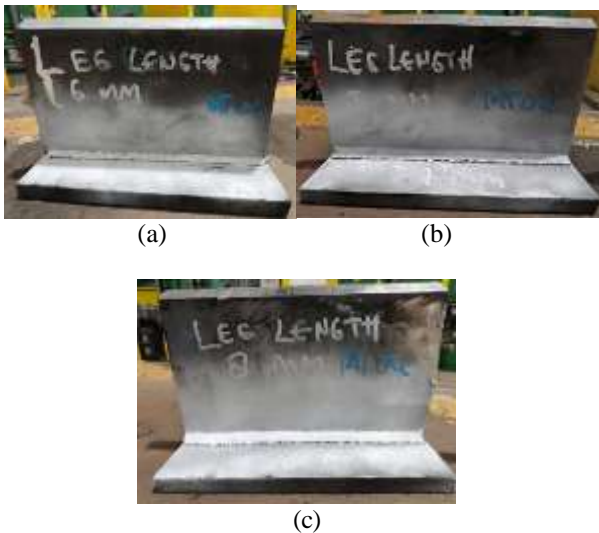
Hasil Percobaan *Leg Length Fillet Weld
